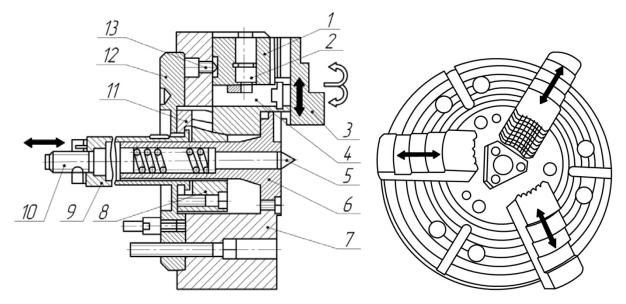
Трехкулачковый клиновой быстропереналаживаемый патрон: 1 — основание кулачка; 2 — эксцентрик; 3 — кулачок; 4 — тяга; 5 — плавающий центр; 6, 14 — сменные вставки; 7 — корпус; 8 — втулка с клиновыми замками; 9 — втулка; 10 — винт; 11, 12 — фланцы; 13 — штифт
